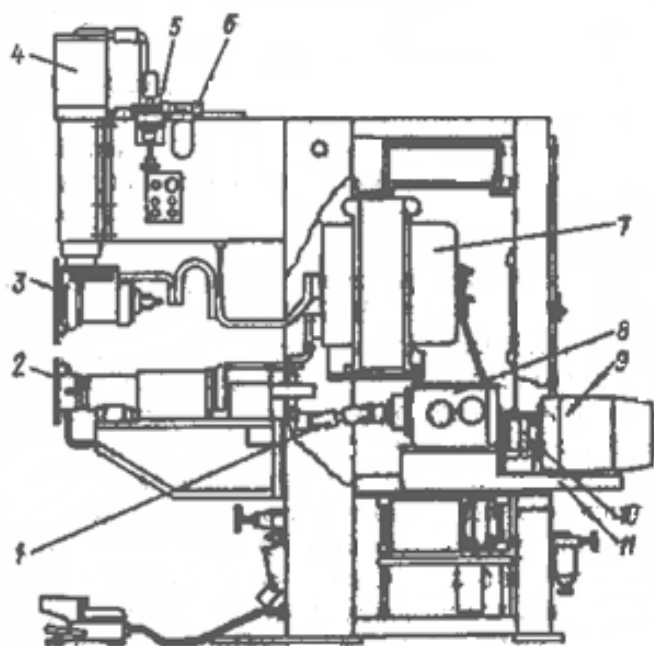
Машина сварочная типа МШ-3207
